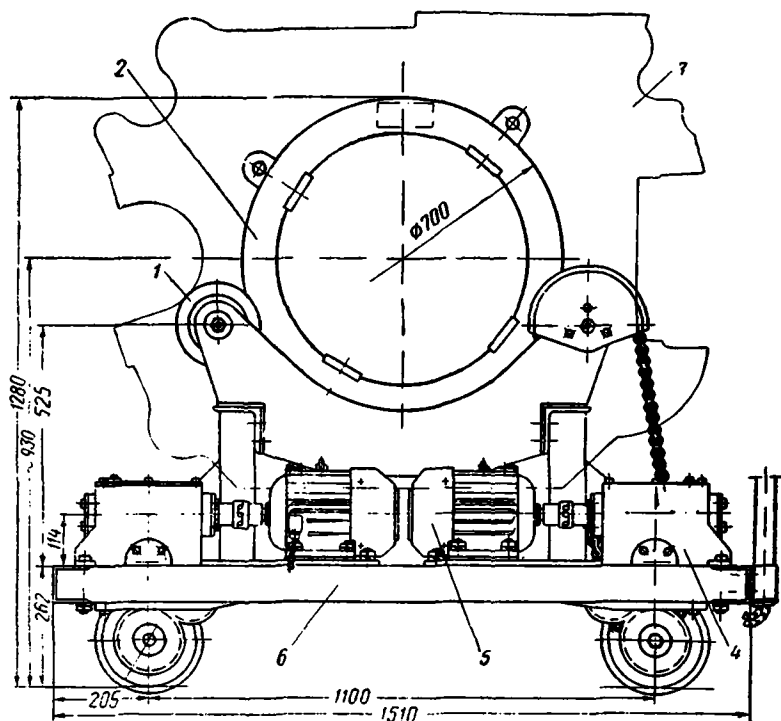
Передвижной кантователь остова тягового двигателя для наплавочных работ:
